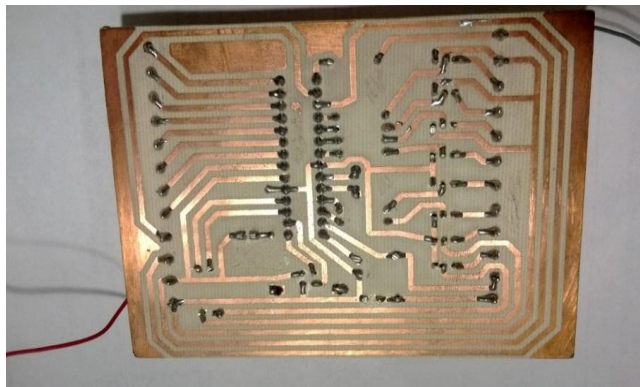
PCB de la DAQ impresa en la placa de cobre con los dispositivos soldados.
